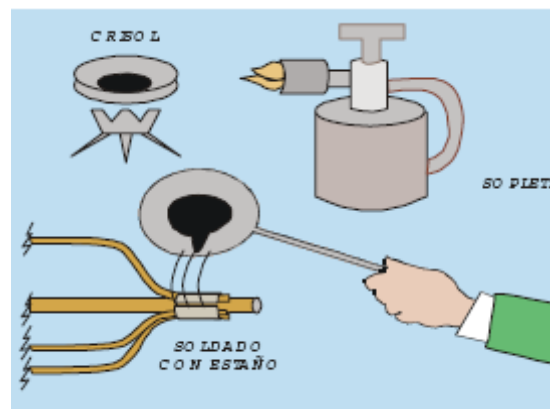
Soldado de electrodos auxiliares.
